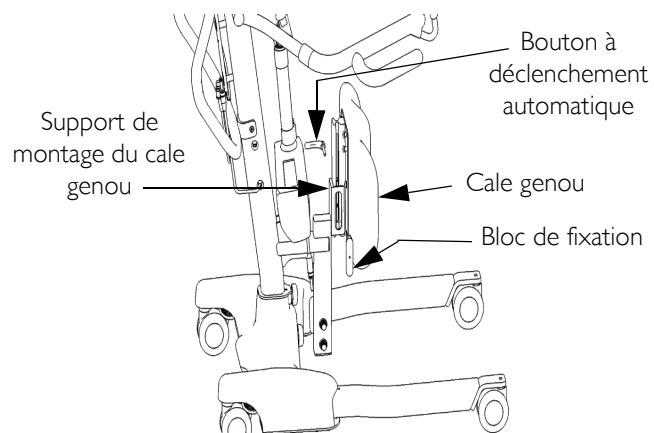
Assemblage du cale genou à l'ensemble du mât
